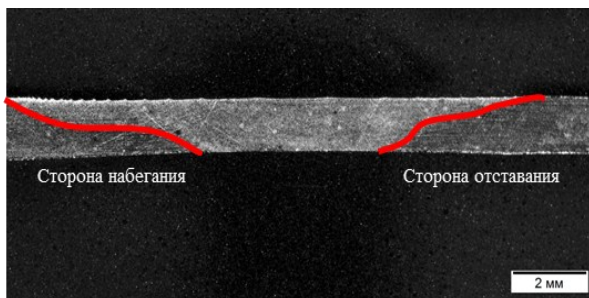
Макроструктура сварного соединения сплава В-1469-Т
